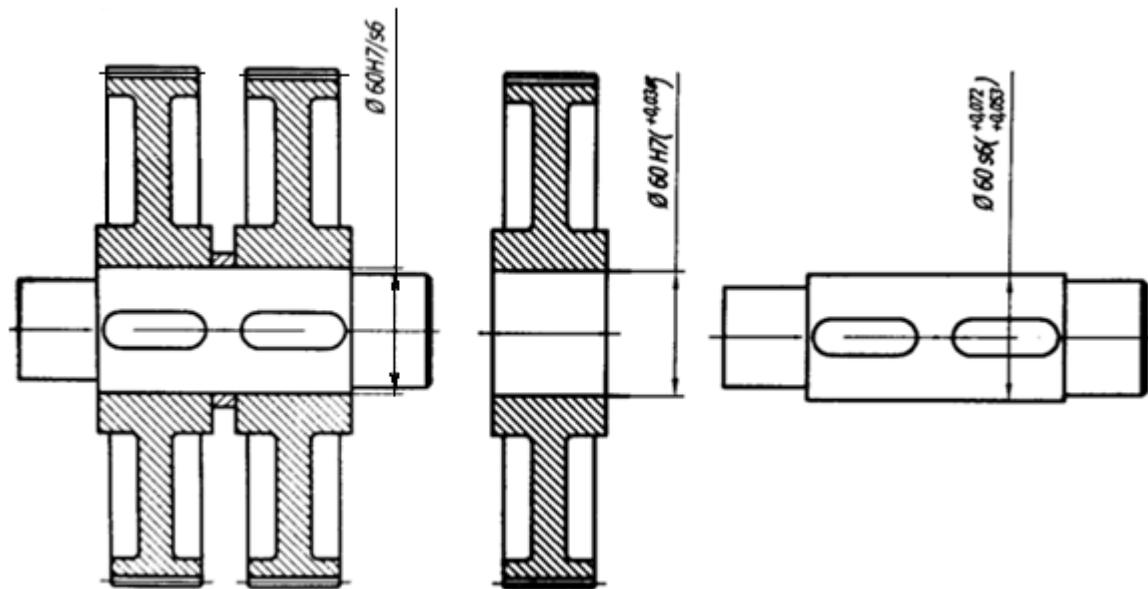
Зубчатые колеса на валу с дополнительным креплением шпонкой
